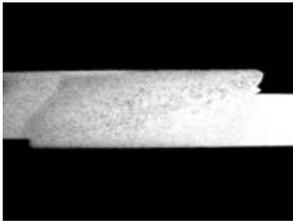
Schweißung mit großer Überlappung; Nahtüberhöhung; Quetschnahtschweißung, Tailored Blank, Dicke 0,8 + 1,1 mm.
